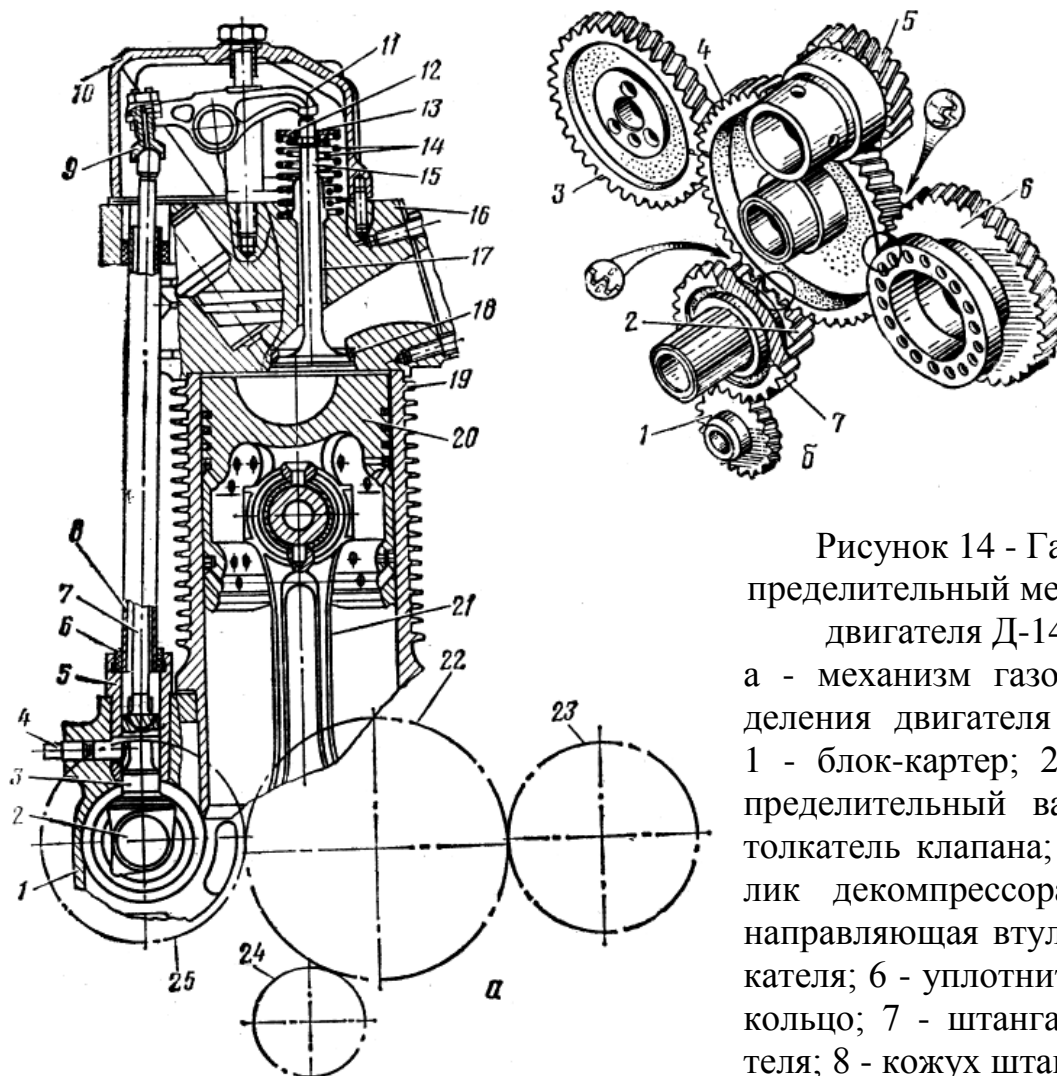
Газораспределительный механизм двигателя Д-144:
